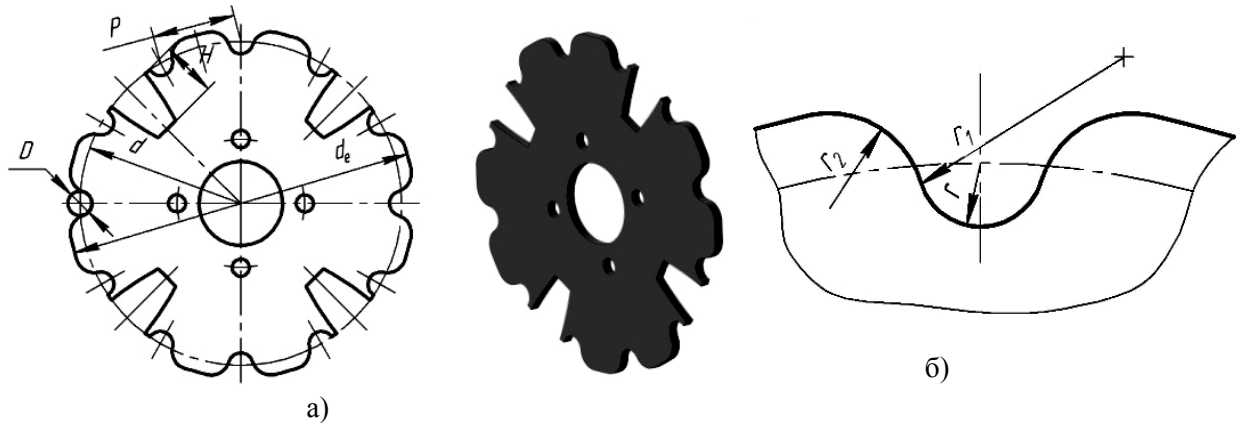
Конструкція спеціальної приводної зірочки: а) зірочка; б) конструктивні параметри впадини
